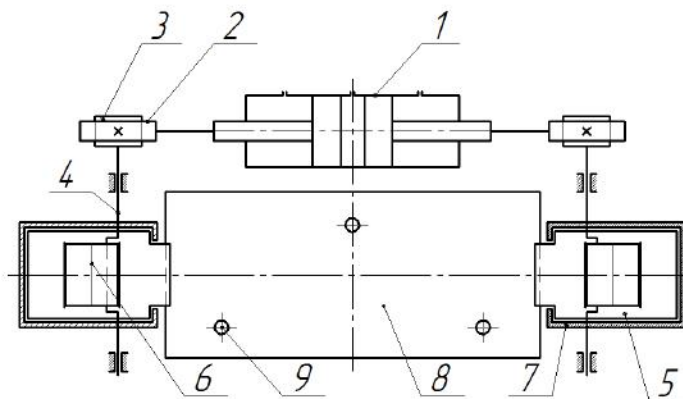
Кінематична схема блока швидкознімного кріплення: 1 – пневмоциліндр двосторонньої дії; 2 – зубчаста рейка; 3 – зубчаста шестерня; 4 – ексцентриковий вал; 5 – затискний повзун; 6 – круговий шатун; 7 – напрямний корпус затискного повзуна; 8 – робоча зона для розміщення штампових пакетів; 9 – фіксуючі елементи для розміщення пакету
